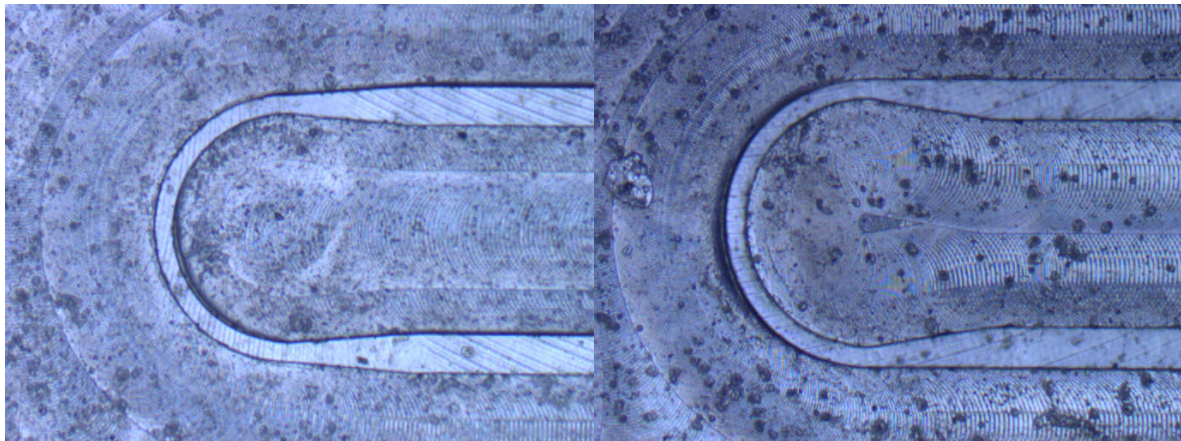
Detailansicht zweier Kanalstrukturen
